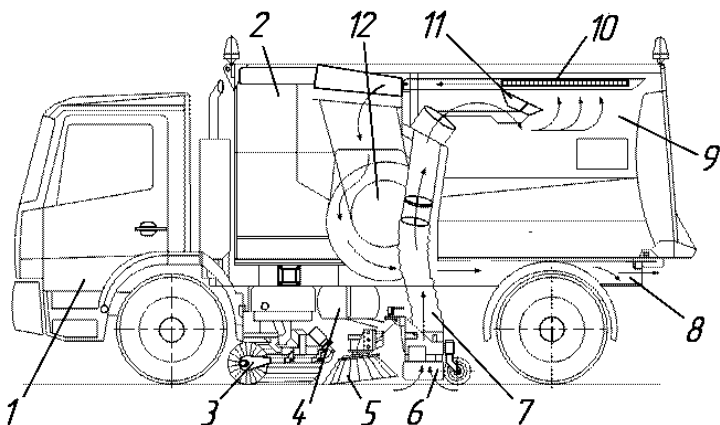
Схема щеточно-вакуумной подметально-уборочной машины:
